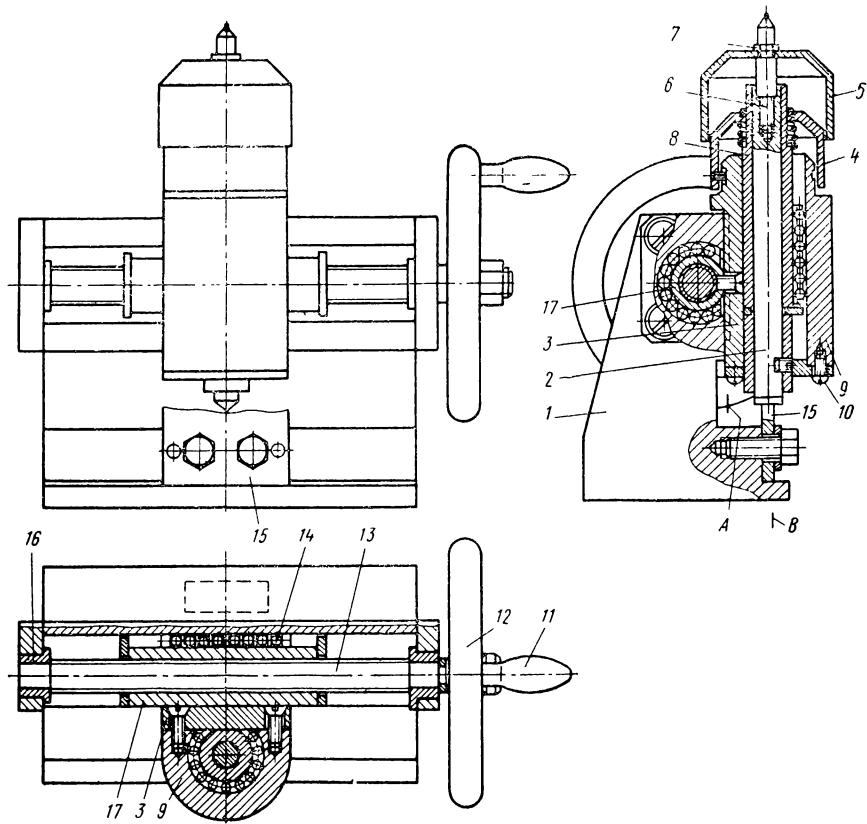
Приспособление к плоскошлифовальному станку для профилирования круга по шаблону
